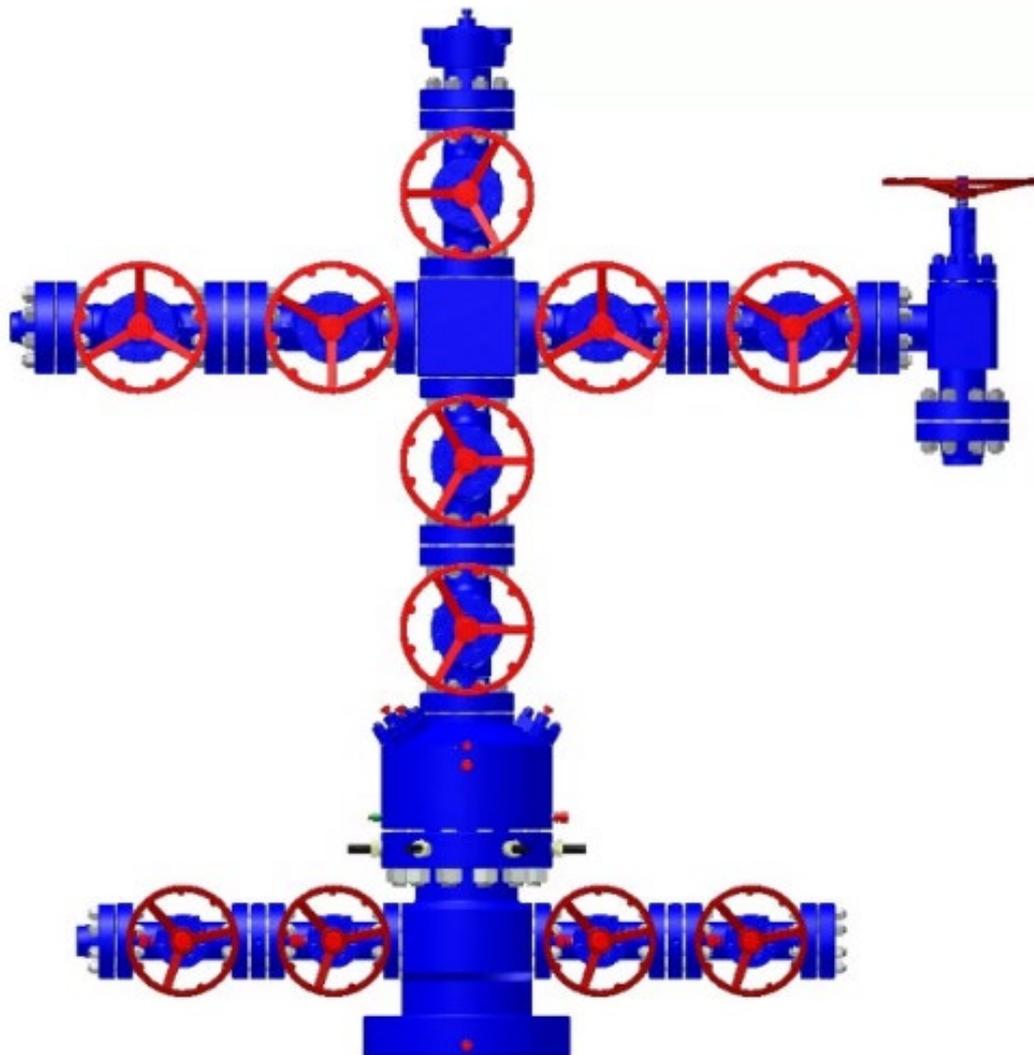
Фонтанная арматура с крестовой елкой
